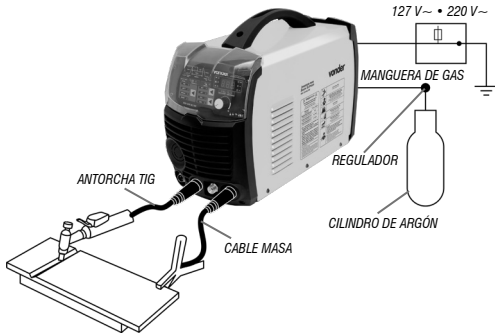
Montaje del conjunto para soldadura TIG
